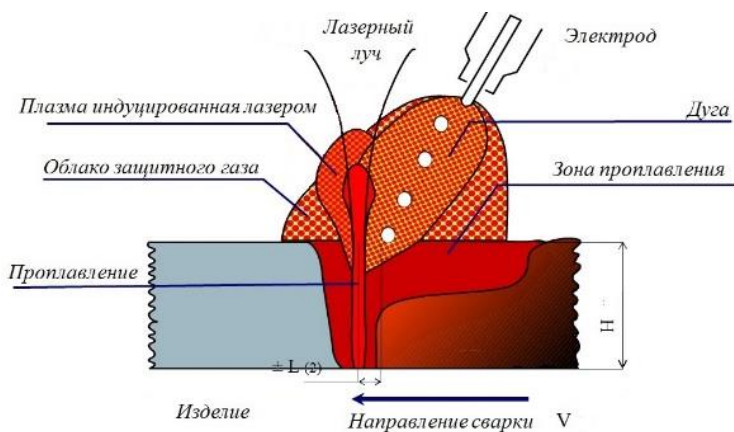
Схема процесса лазерно-дуговой сварки
